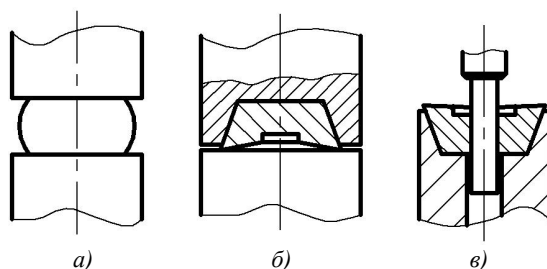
Последовательность изготовления заготовки долбяка: а) осадка; б) объемная штамповка; в) прошивка отверстия
